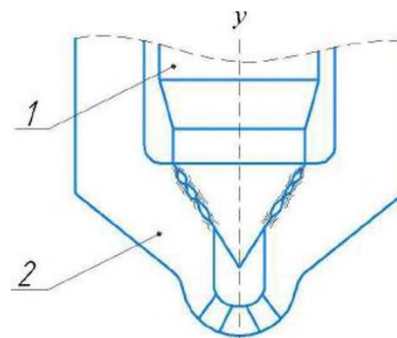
Схема процесу формування мікротріщин у поверхневому шарі сполучення "голка – корпус розпилювача форсунки": 1 – голка; 2 – сідло корпусу розпилювача форсунки [22].
